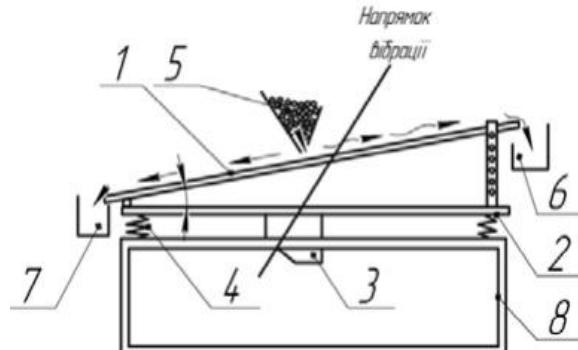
Принципова схема сепаратора з циліндричною робочою поверхнею
